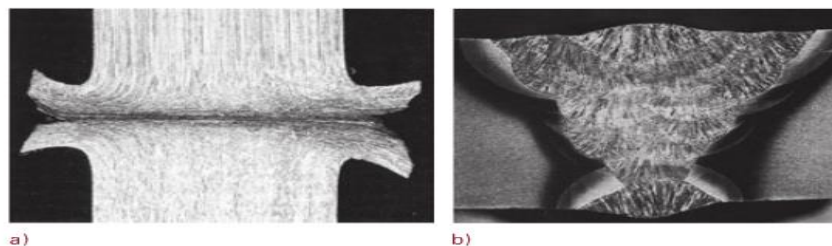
a) Soldadura no estado sólido; b) Soldadura por fusão.
